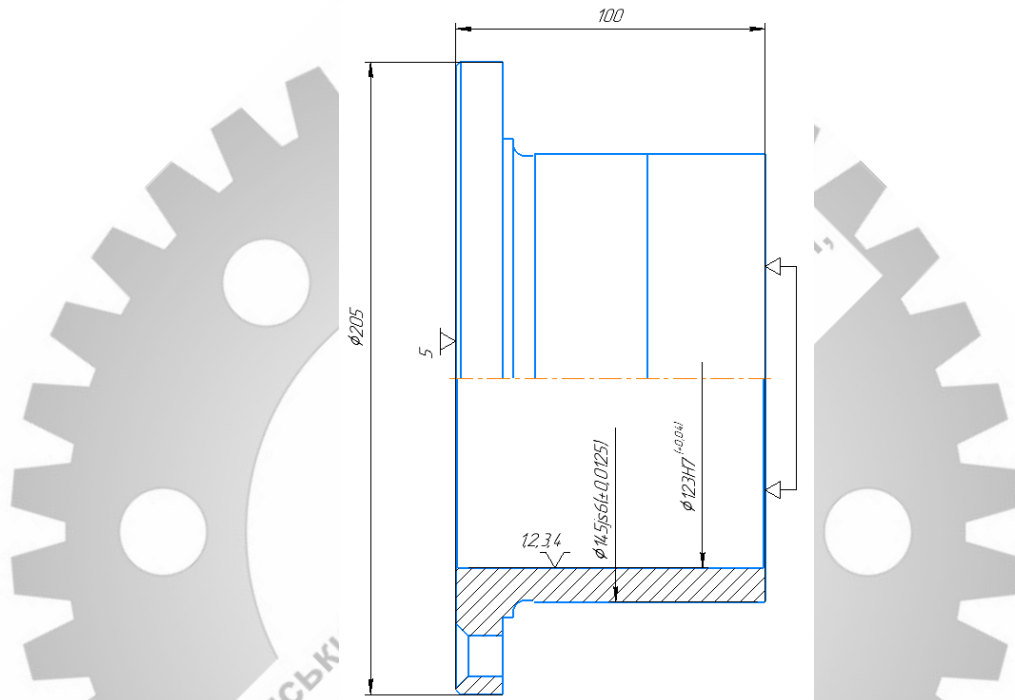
Схема базування деталі у 3-х кулачковому патроні на операції 055
